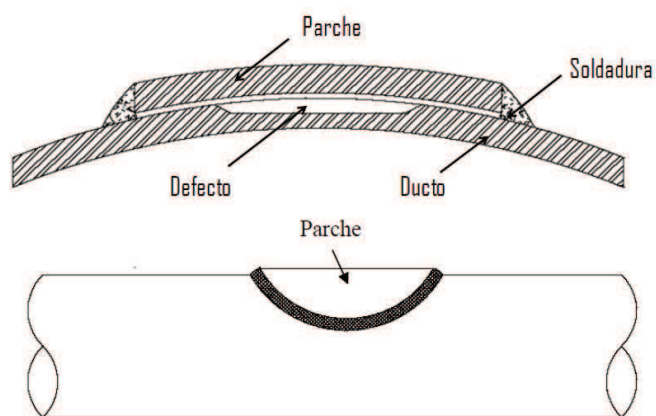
Parche soldado en una tubería^[5].
